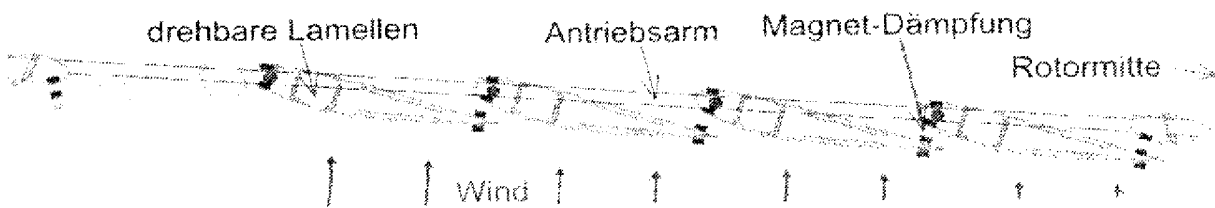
Oben- Draufsicht des Rotors, Lamellen Dämpfung
